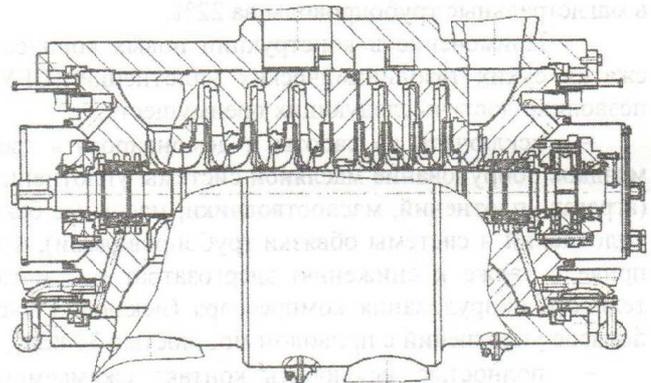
Разрез корпуса 4ГЦ2-184/13,5-76
